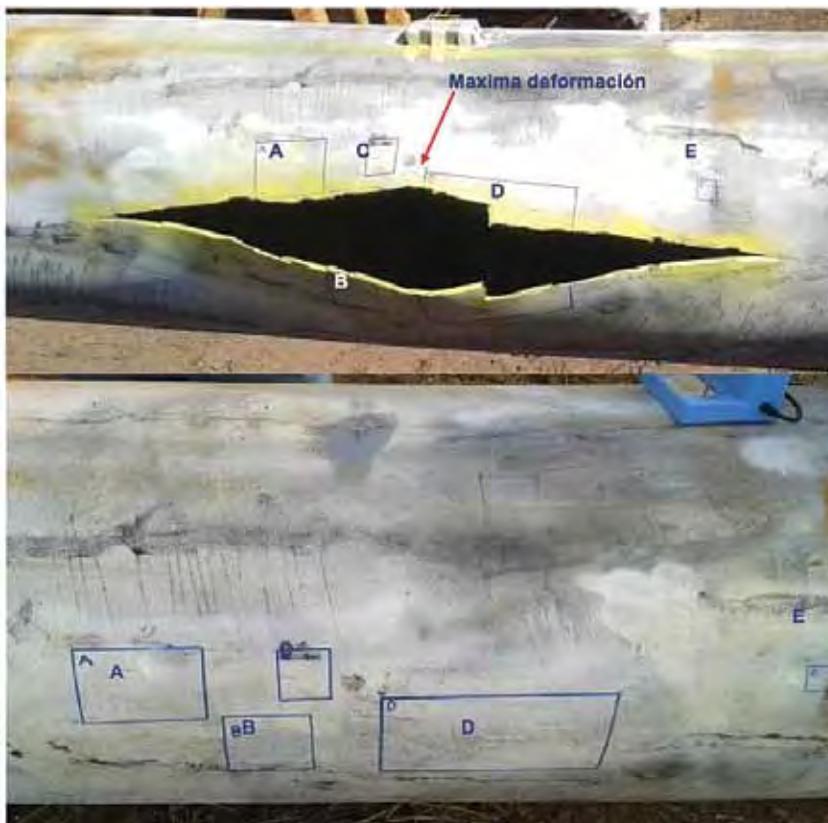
Grupo de fisuras en el caño extraído para la prueba hidráulica a rotura.
